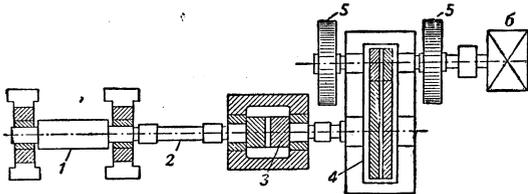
Рабочая линия стана: 1 — рабочая клетка, 2 — соединительные шпиндели, 3 — шестеренная клетка, 4 — редуктор, 5 — маховик, 6 — двигатель.
